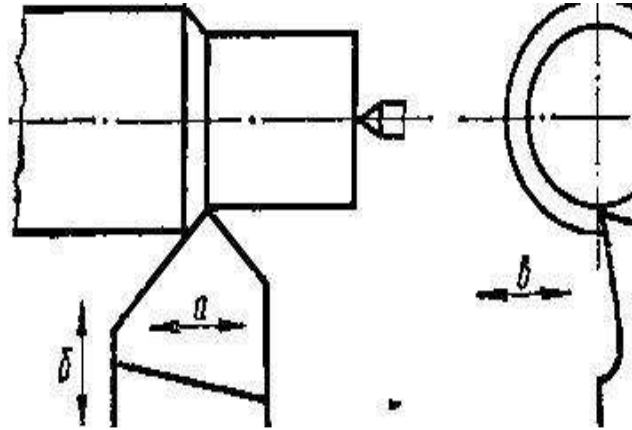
Вібраційний рух інструменту під час обробки
